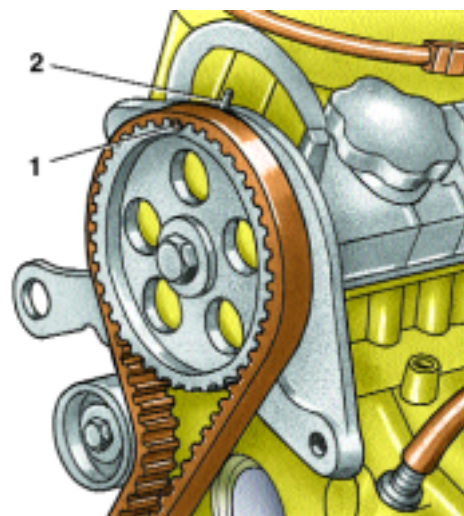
Установка поршня 1-го и 4-го цилиндров двигателя F3R 272 в положение в.м.т.
